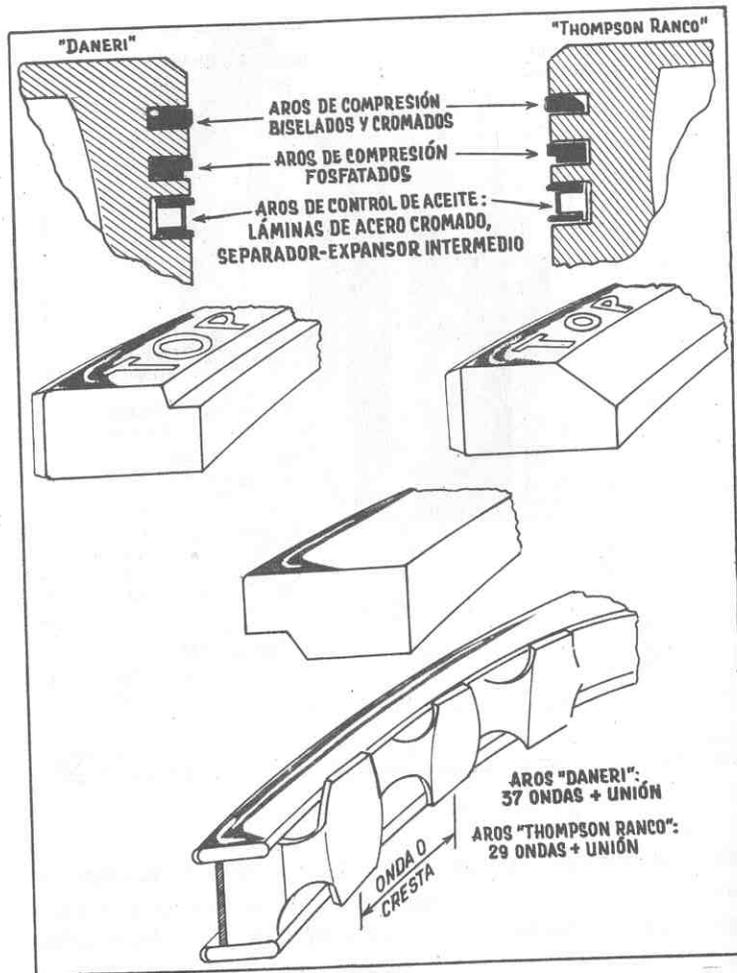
Detalles de los aros y su colocación en el pistón.
